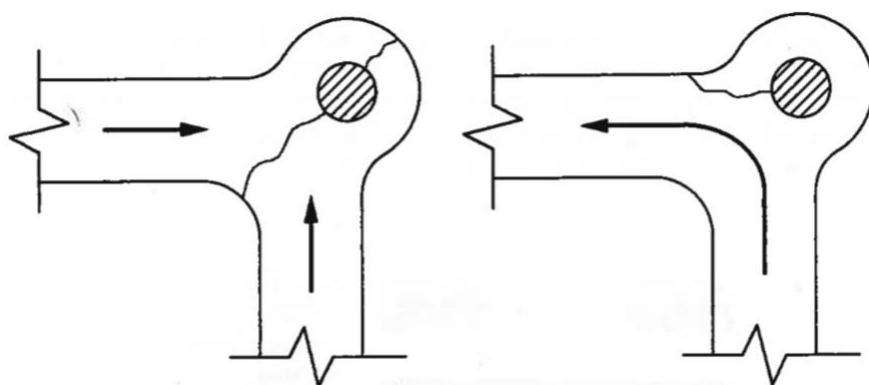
Zonas em que uma linha de soldadura pode ser crítica [9].
